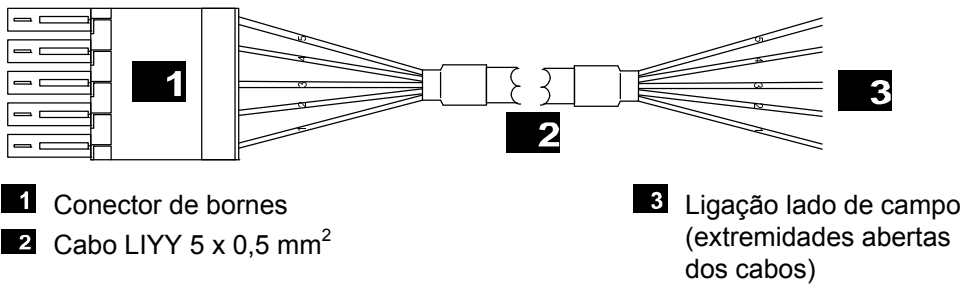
Cabo do conjunto de cabos de sistema X-CA 004 02
